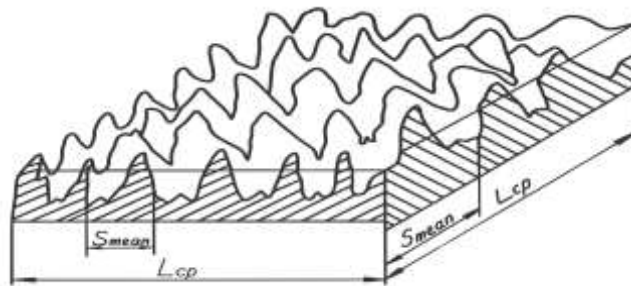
Форма контактуючої поверхні зуба колеса
